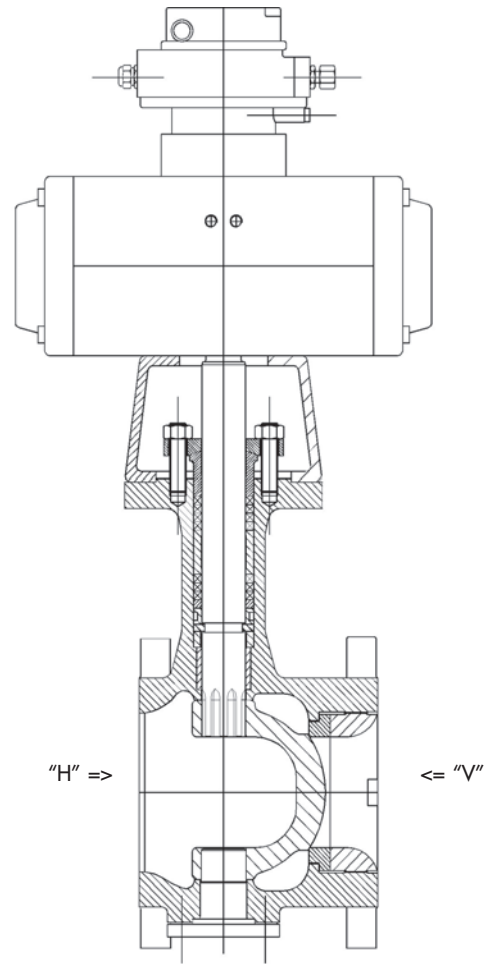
· Vue en coupe vanne VETEC Type 72.4/AT montage sandwich
